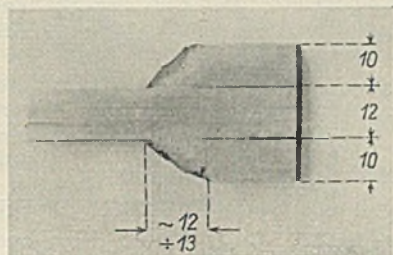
Längsschnitt durch eine elektrisch geschweißte Stirnkehlnaht-Laschenprobe.
